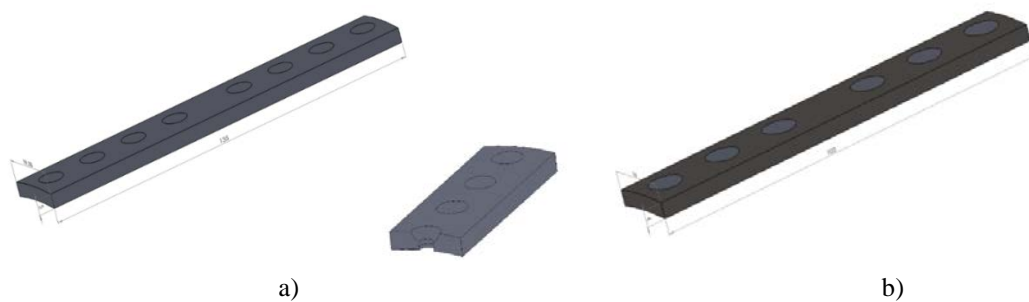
Modelo 3D das placas de furos redondos (dimensões em mm): a) Placa de oito furos com pormenor do furo; b) Placa de seis furos.
